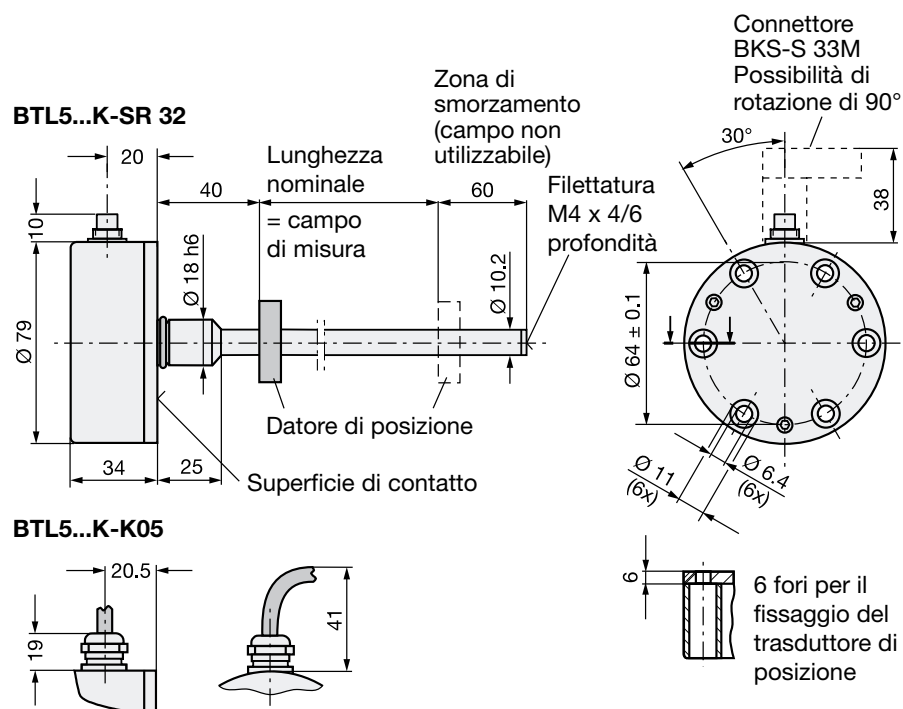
Trasduttore di posizione BTL5...K..., disegno quotato
